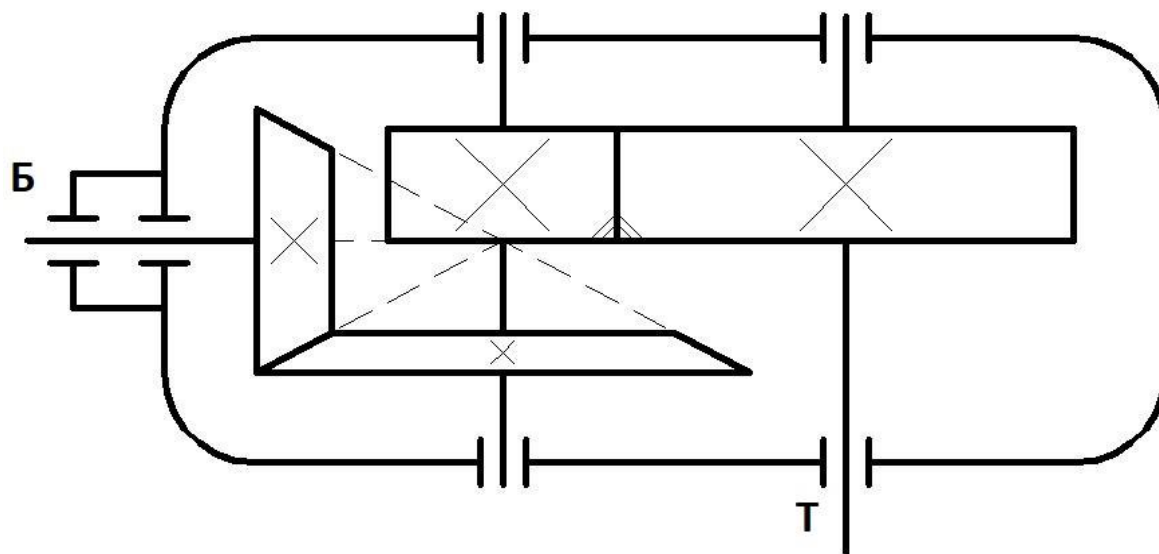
Схема коническо-цилиндрического редуктора
